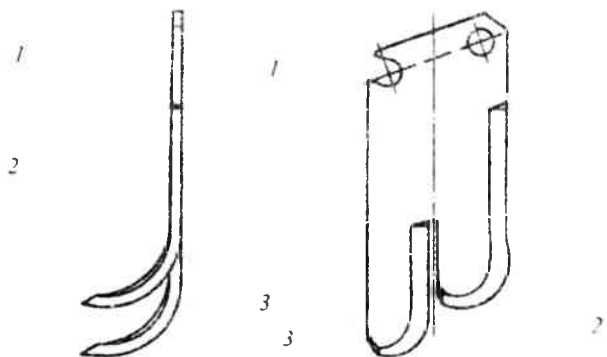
Нож со ступенчато расположенными лезвиями:
